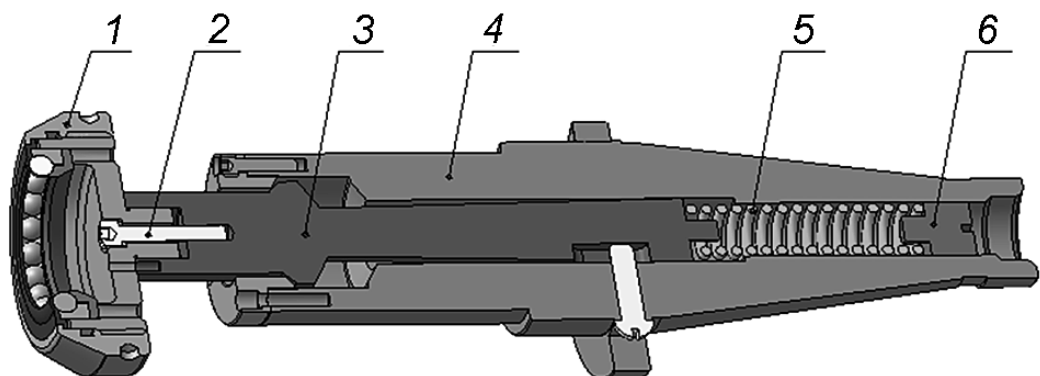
Инструмент, для обкатывания (1- обкатник, 2- винт, 3 – шток, 4 – корпус, 5- пружина, 6 – регулировочный винт).
